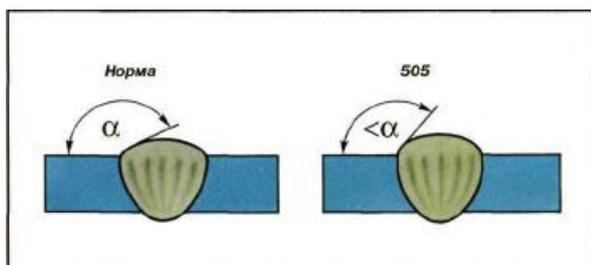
Неправильный профиль сварного шва. (Код дефекта: 505)
